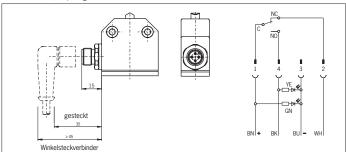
Maßzeichnung/Anschlussplan N01.550C1526 mit Steckverbinder M12 (4-polig)
